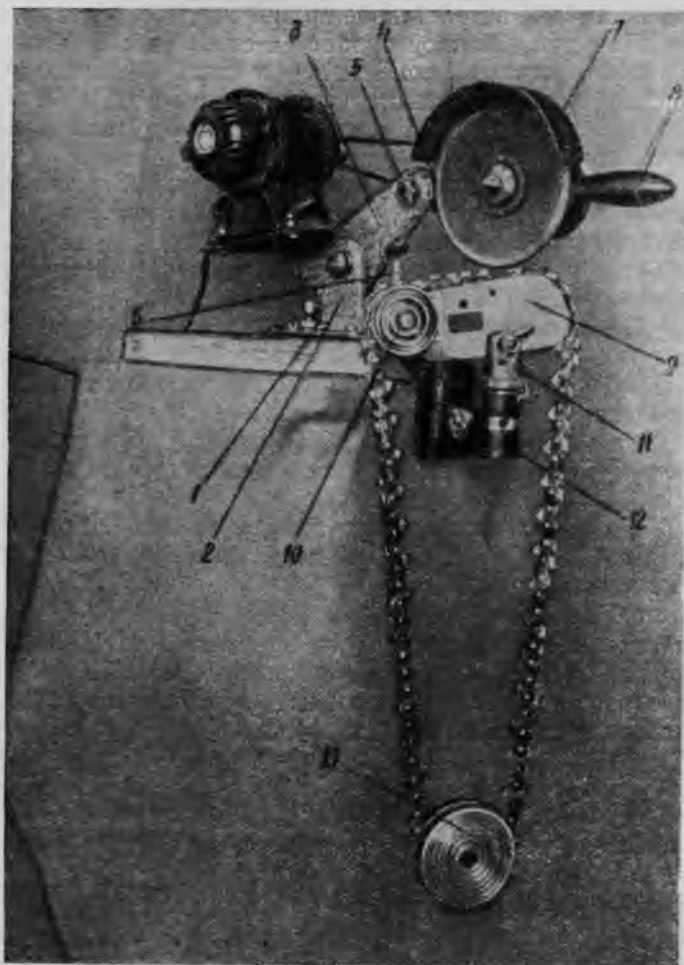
Заточно-фуговочный станок ЦНИИМЭ:
